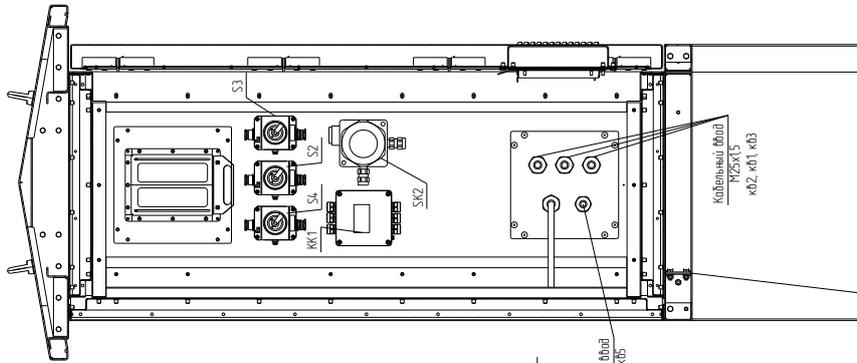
ТШВ-15157. Чертеж общего вида.
